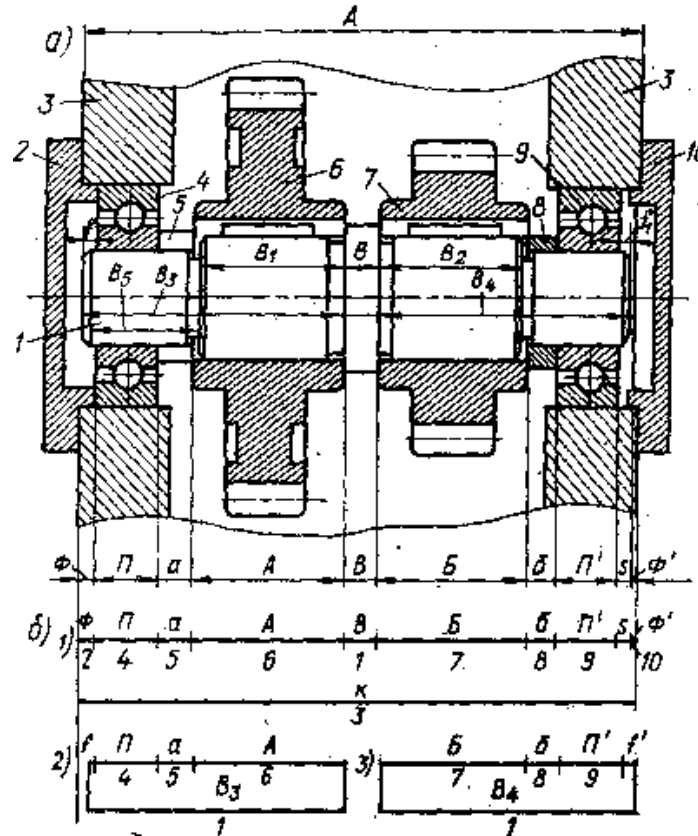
Сборочный чертёж узла (а) со сборочными цепями
